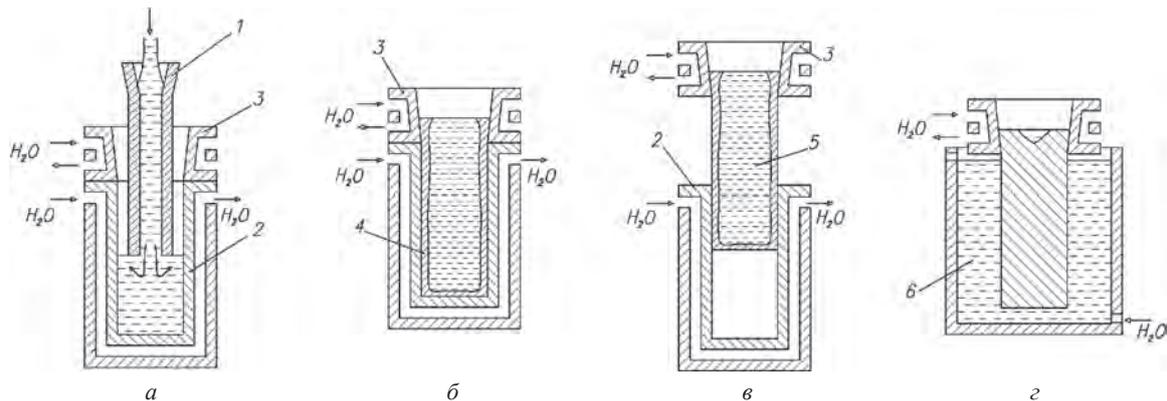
Схема литья закалочным затвердеванием: а – заполнение кристаллизатора; б – формирование стакана; в – извлечение стакана с расплавом; г – закалочное затвердевание – получение отливки; 1 – заливочное устройство; 2 – стационарный кристаллизатор; 3 – подвижный кристаллизатор; 4 – стакан; 5 – расплав; 6 – закалочная ванна
